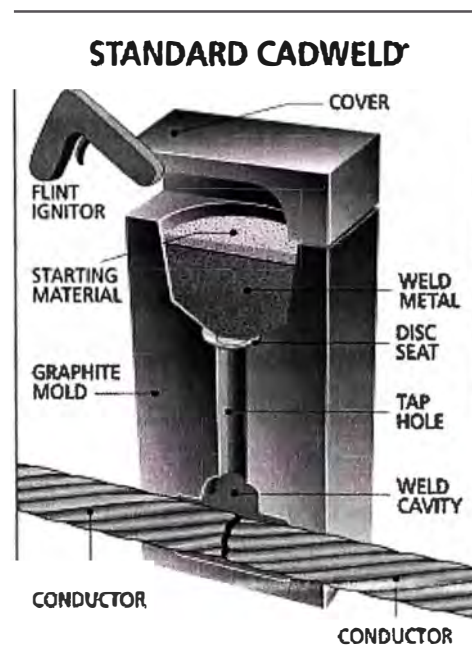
Molde para Soldadura Cadweld
